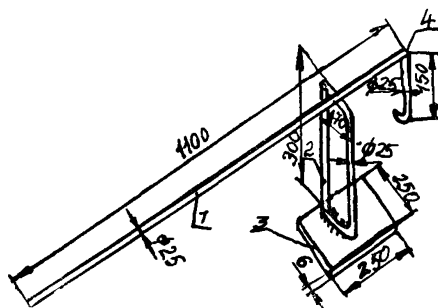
Приспособление для подъема рельс-форм при рихтовке:
